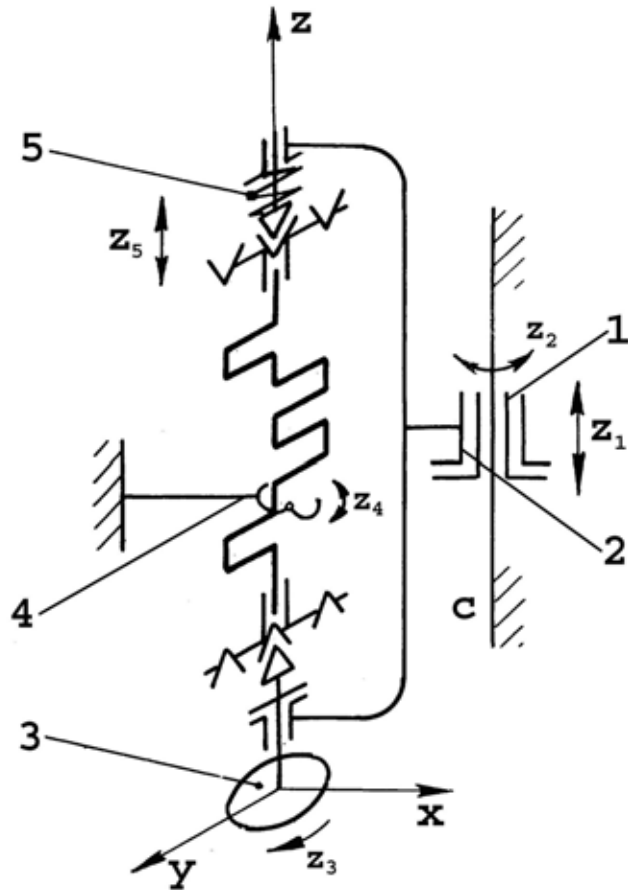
Схема станда для закалки шеек коленчатого вала: С – станина; 1 – механизм осевого перемещения детали; 2 – механизм введения шейки вала в индуктор; 3 – механизм вращения детали; 4 – индуктор; 5 – пиноль
